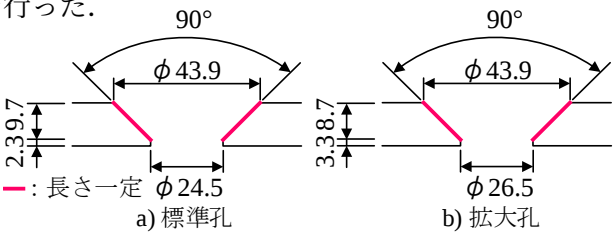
ボルト孔径の違いによる皿型加工深さ (単位：mm)
